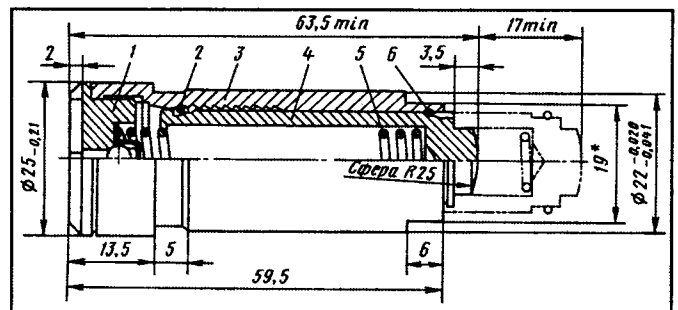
Гидравлический натяжитель цепи: 1 — резьбовая крышка корпуса; 2 — запорное кольцо; 3 — корпус; 4 — поршень; 5 — пружина; 6 — стопорное кольцо
